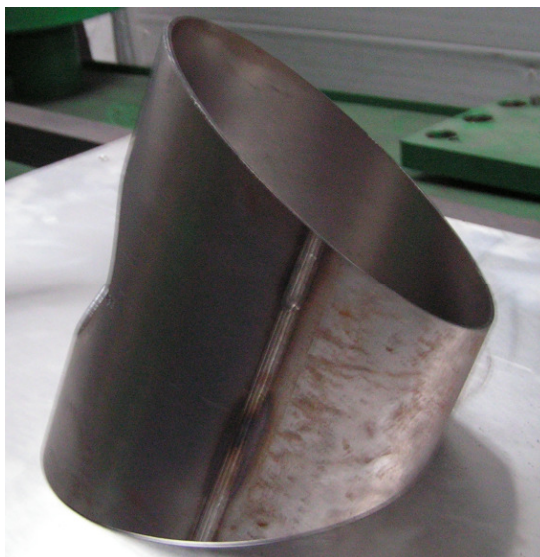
Prawidłowe obręcze spełniające warunki odbioru technicznego
